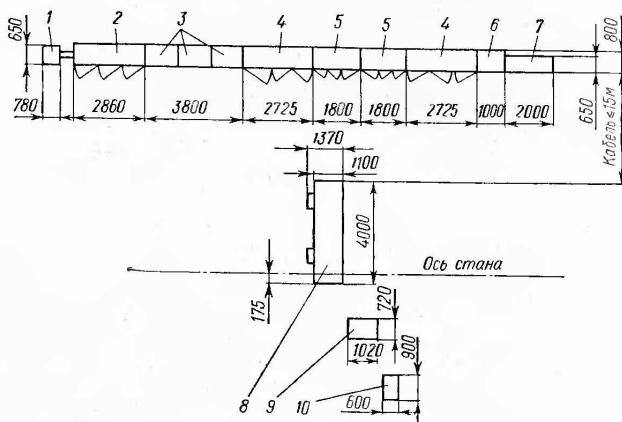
Расположение блоков высокочастотной сварочной установки ВЧС1-630/0,44:
